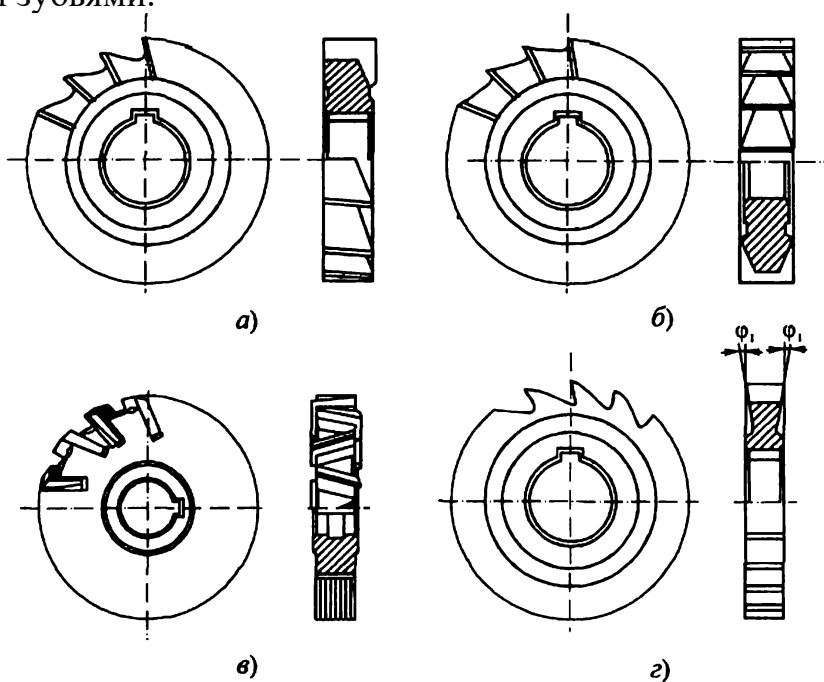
Виды дисковых фрез: а – двусторонняя; б – трехсторонняя; в – трехсторонняя с разнонаправленными вставными зубцами; г – пазовая
